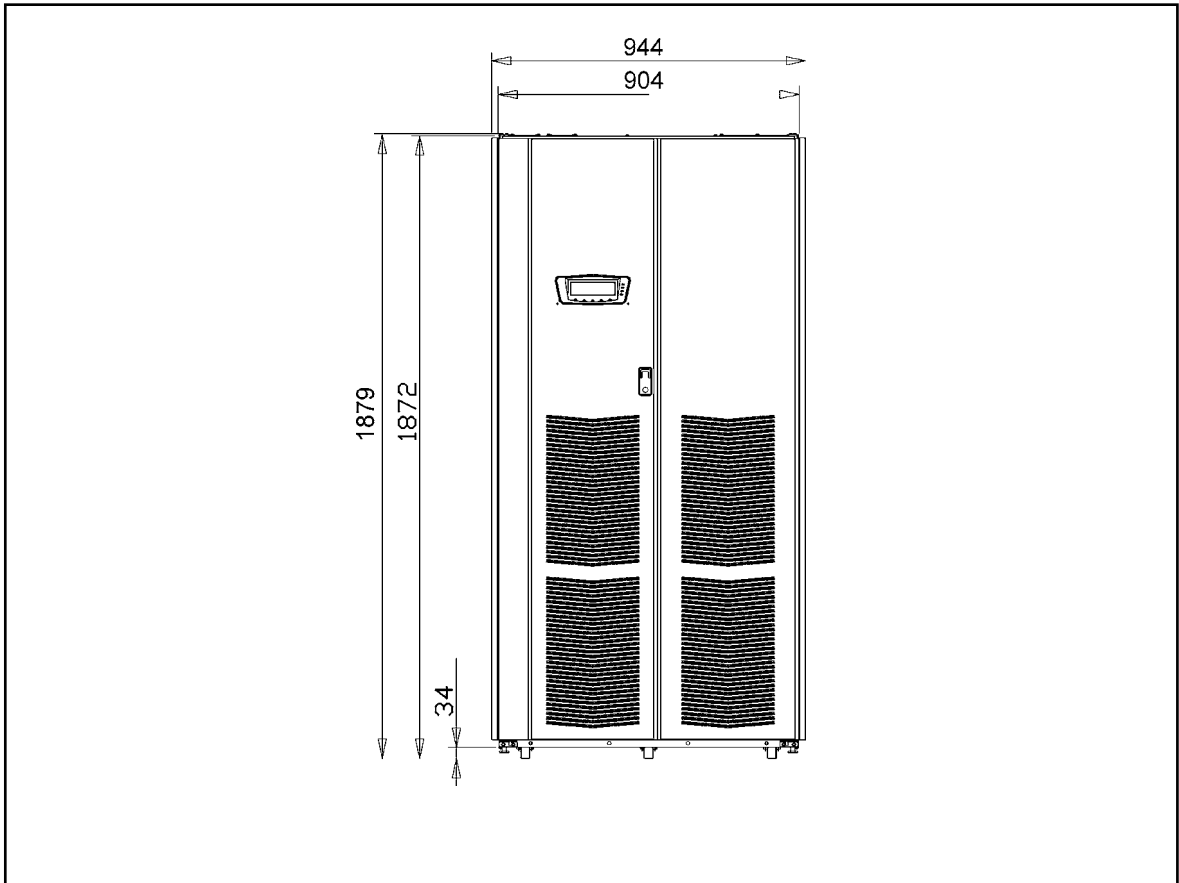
Abmessungen – USV-Schrank (100-160 kVA)
